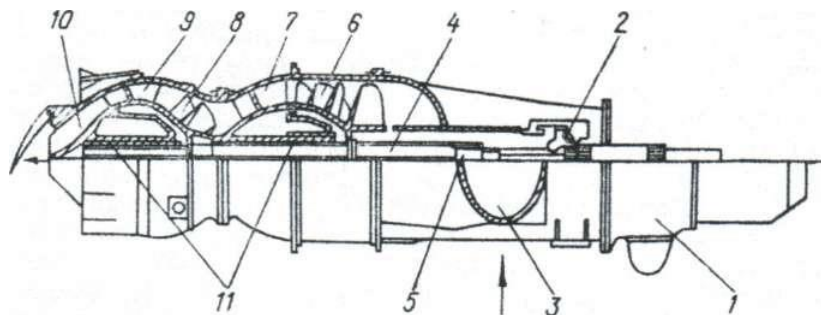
Насосная установка основного водометного движителя корабля класса РНМ (США). 1 – редуктор; 2 – упорный подшипник; 3 – входное отверстие; 4 – вал первой ступени; 5 – вал второй ступени; 6 – рабочее колесо первой ступени; 7 – спрямляющий аппарат первой ступени; 8 – рабочее колесо второй ступени; 9 – спрямляющий аппарат второй ступени; 10 – выходное сопло; 11 – подшипники скольжения
